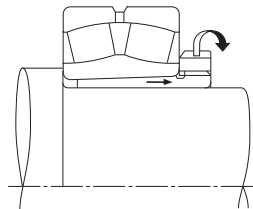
Demontage einer Abziehhülse mit Abziehmutter (1)
